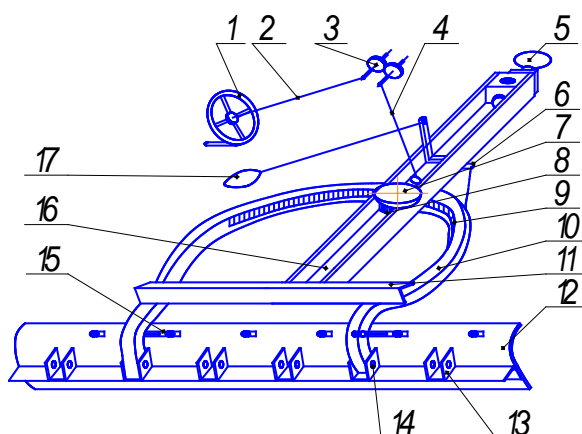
Схема рабочего органа и механизма поворота отвала грейдера ДЗ-1: 1 — штурвал, 2 — соединительный вал, 3, 8 — шестерни, 4 — телескопический вал, 5 — шарнирное звено, 6 — защелка, 7 — редуктор, 9 — зубчатый сектор, 10 — поворотный круг, 11 — тяговая рама, 12 — отвал, 13 — проушина, 14 — палец, 15 — гребенка, 16 — шкворень, 17 — тяга
